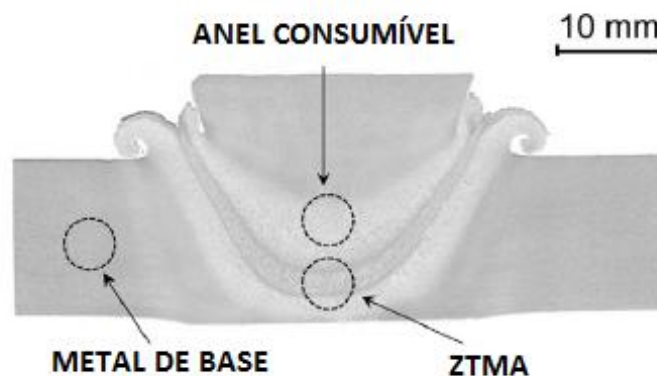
Seção longitudinal da junta soldada por SFR
